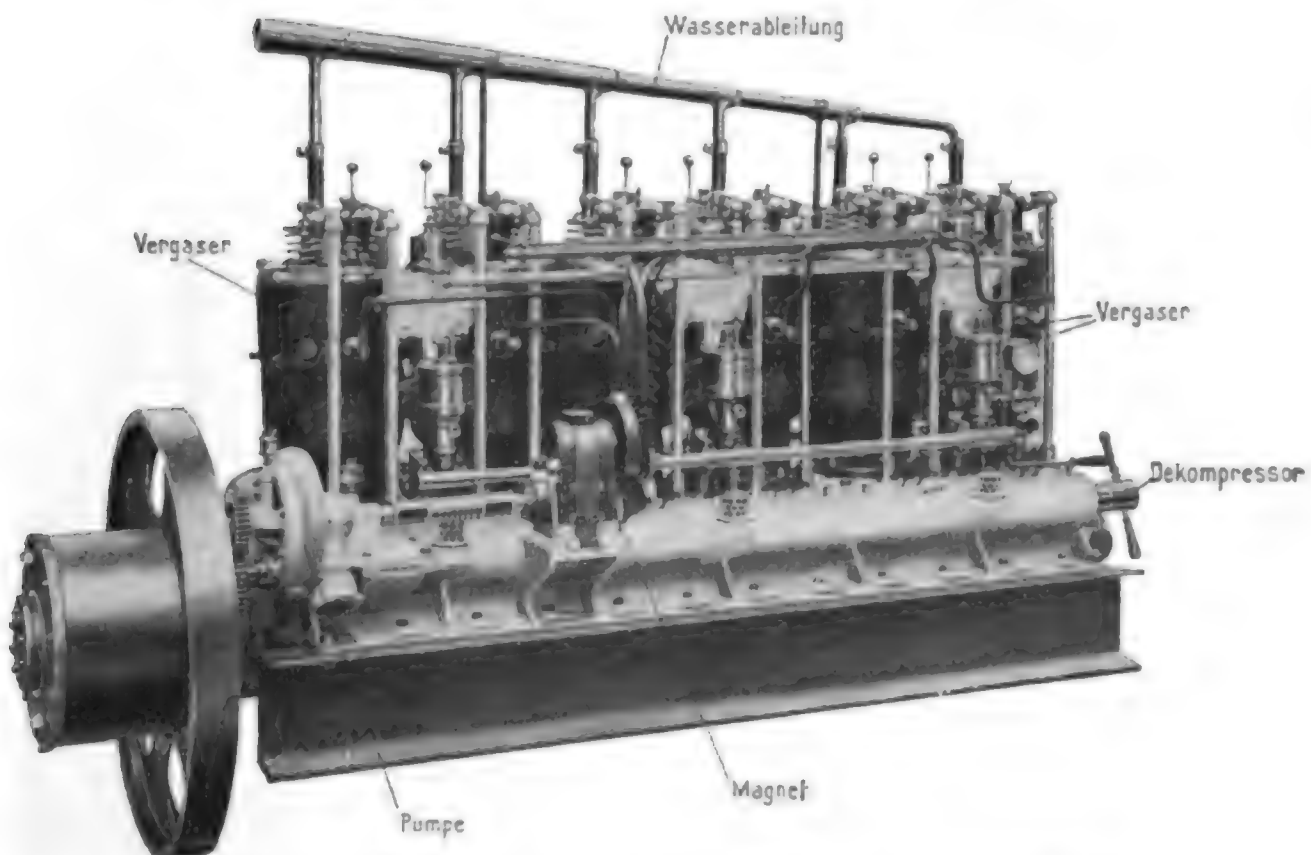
Luftschiffmotor der N. A. G., Ansicht von der Seite der Steuerwelle.
